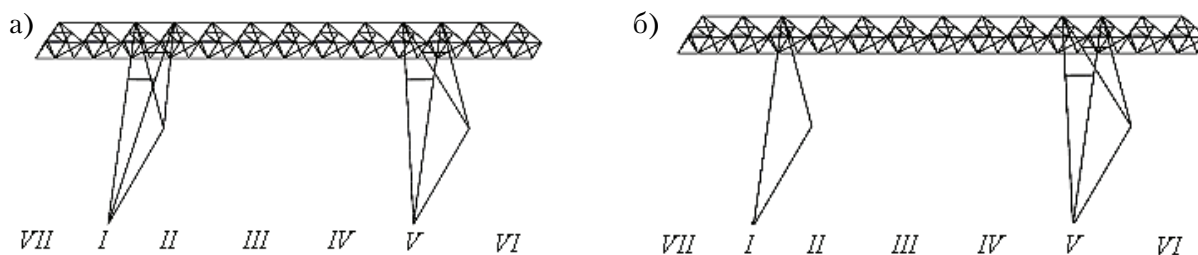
Расчетные схемы козлового крана КК-12,5-25 с двумя жесткими опорами (а) и одной жесткой, а другой гибкой опорами (б).
